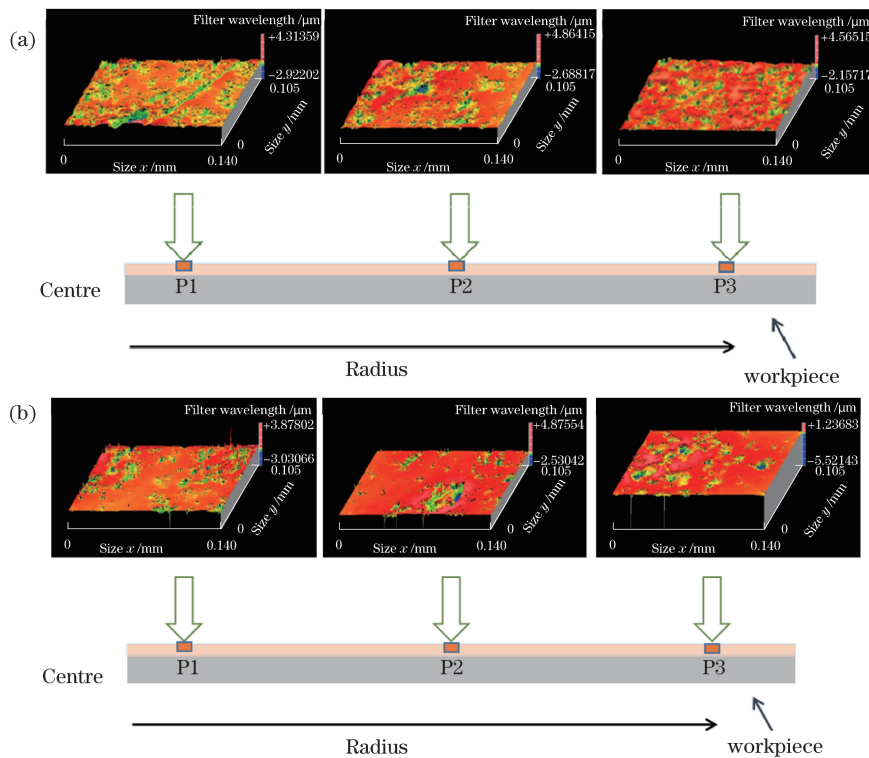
两种磨盘加工工件形貌。(a) GGP 加工工件表面形貌;
